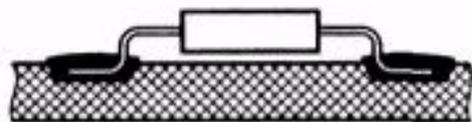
Установка и пайка ЭРИ с плоскими планарными выводами и ПМК в металлизированную ламель
